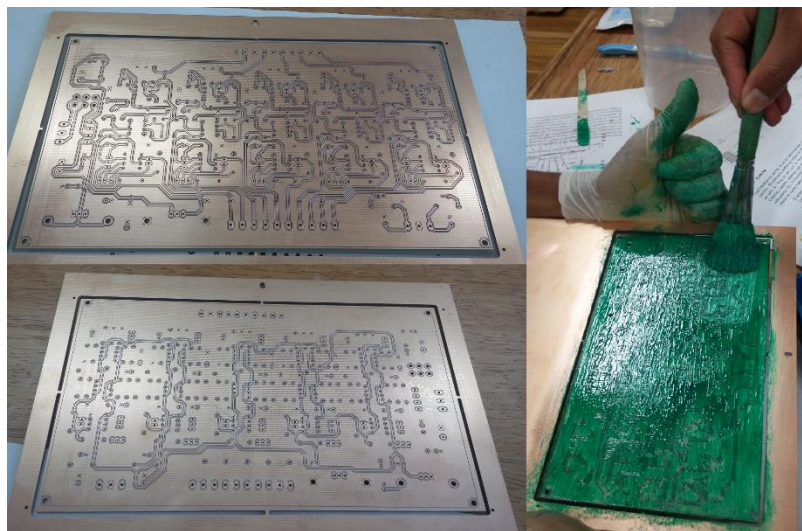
5: Diseño fabricado en placas de material RF4 doble cara de la marca LPKF, vista de la capa Top y Bottom y serigrafía.
